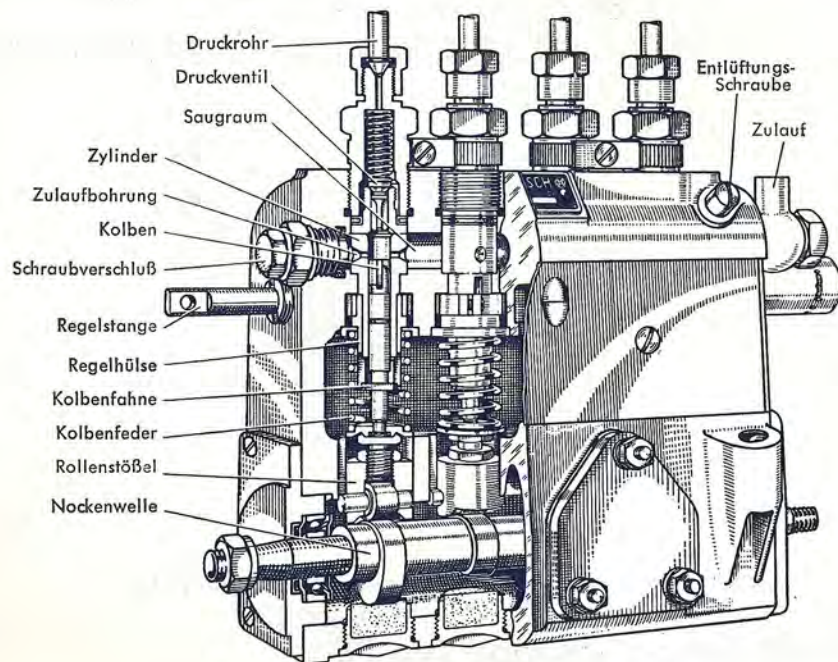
PE..A-Einspritzpumpe für 4-Zylinder-Motor
